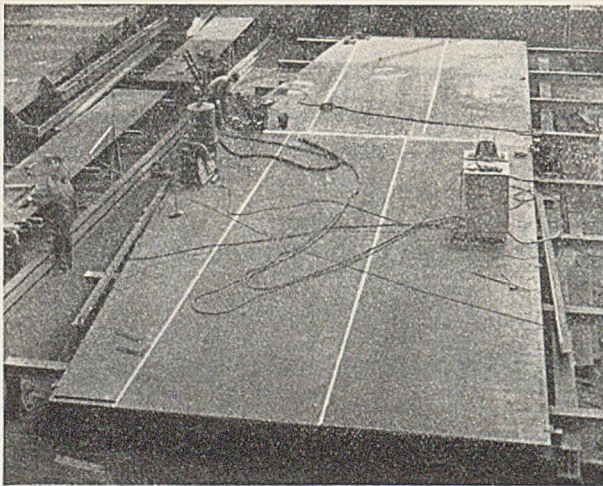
Arbeitsplatz 1. Die Stumpfstöße der Stegbleche und der Gurtungen werden einschließlich der Wurzellage fertig verschweißt. Nach dem Schweißen der Stegbleche werden diese angezeichnet, die obere und untere Stegblechkante mit der Maschine gebrannt und die Brennschnitte leicht abgeschmirgelt.
